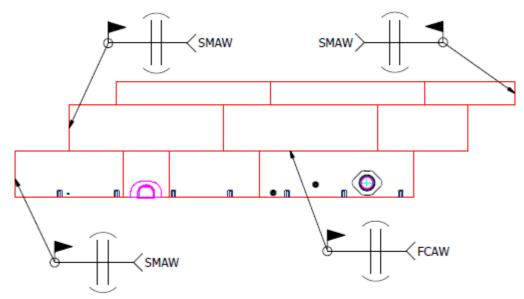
Especificación de soldadura para el cuerpo del tanque.
